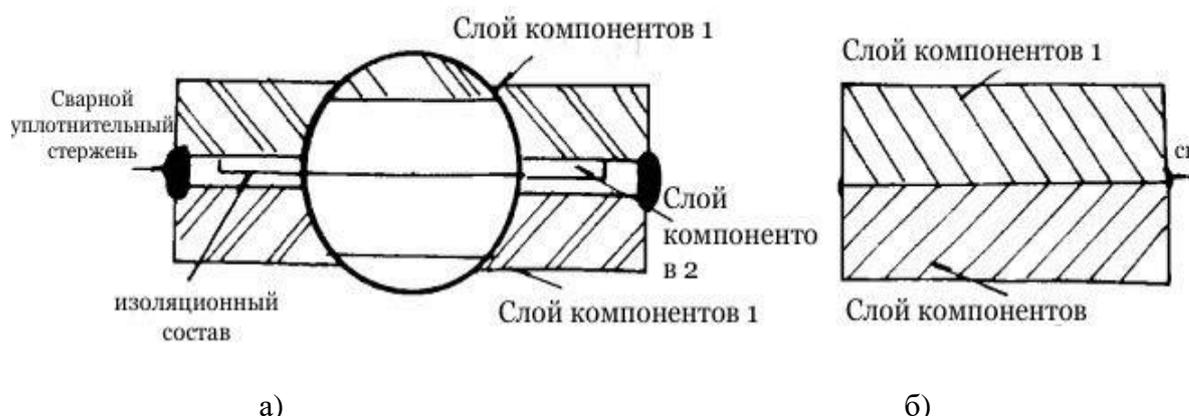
Горячекатаный композитный общий сборочный материал:
